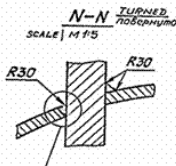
DETALHE DA SOLDA ORIGINAL
